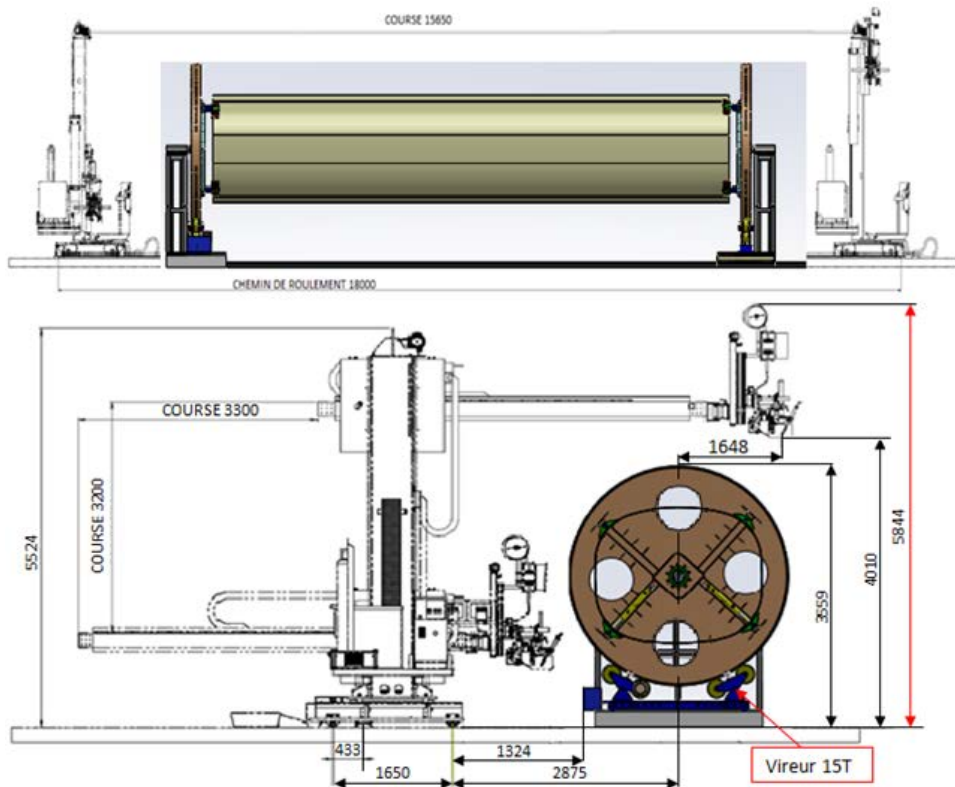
l'emplacement du dispositif avec la soudeuse.
